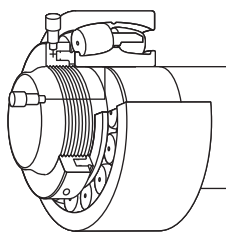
Tuerca hidráulica que se utiliza para montar el rodamiento sobre un eje cónico.
